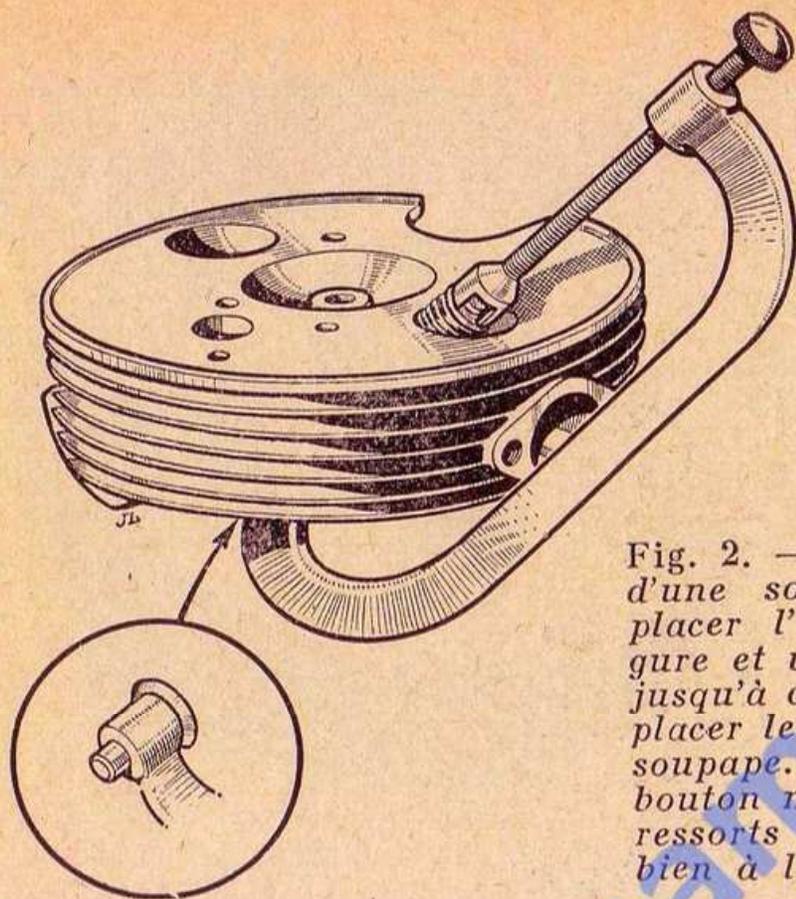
Montage - Démontage d'une soupape. Au remontage placer l'appareil suivant la figure et visser le bouton moleté jusqu'à ce qu'il soit possible de placer les clavettes de queue de soupape. Avant de redévisser le bouton moleté s'assurer que les ressorts et les clavettes sont bien à leurs places respectives.
